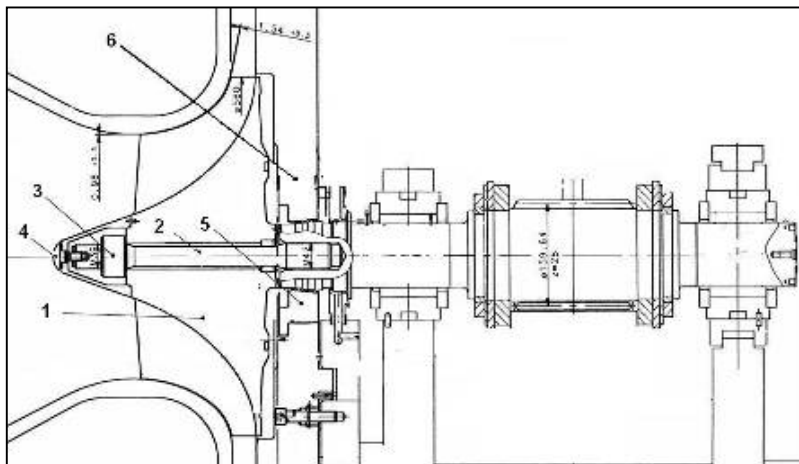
Detalhe do 3º estágio do compressor.⁽²⁾
